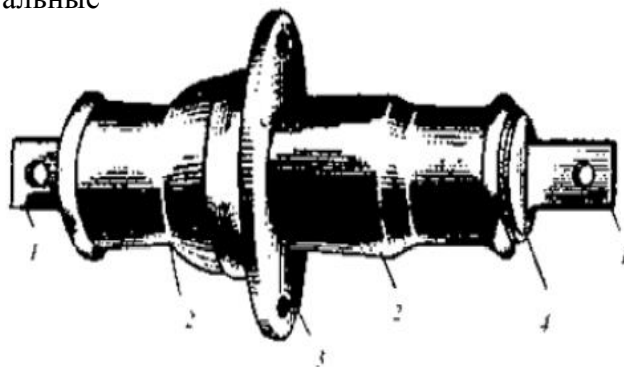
Проходной изолятор ПБ-10/600 для внутренней установки.
